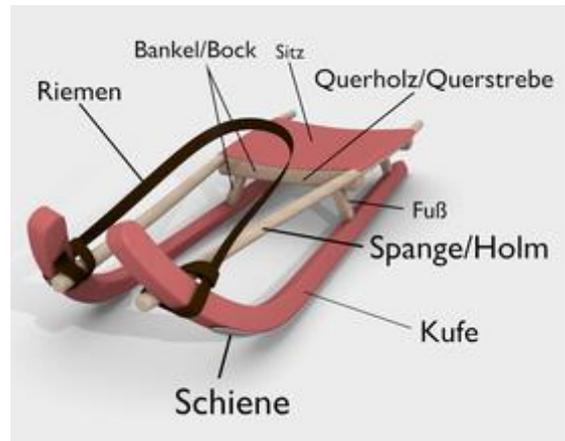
/ Aufbau (rodeln-schweiz.ch, 2023)
